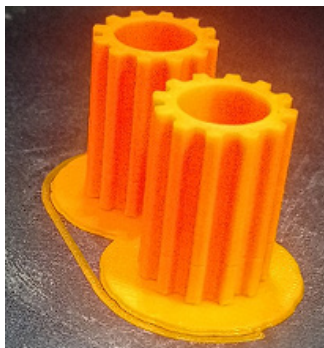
Шестерни мясорубки малые 13 зубьев из ABS-пластика
